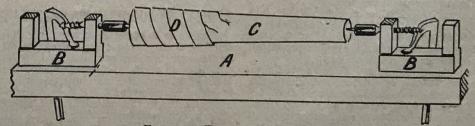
Placage A LA SANGLE: A, établi ; B, presses avec pointes ; C, colonnette à plaquer ; D, sangle enroulée.
